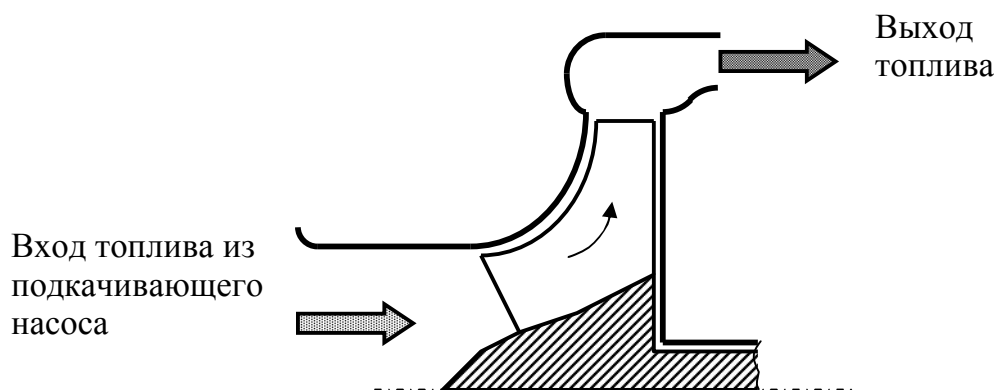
Схема центробежного топливного насоса высокого давления с крыльчаткой открытого типа
